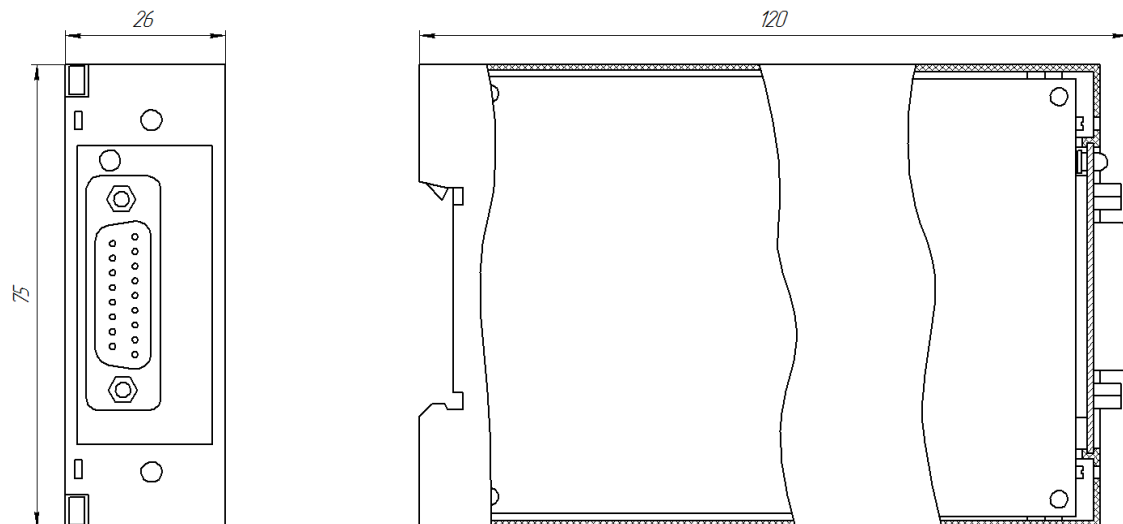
Зовнішній вигляд і габаритні розміри блоку БПТ-22
